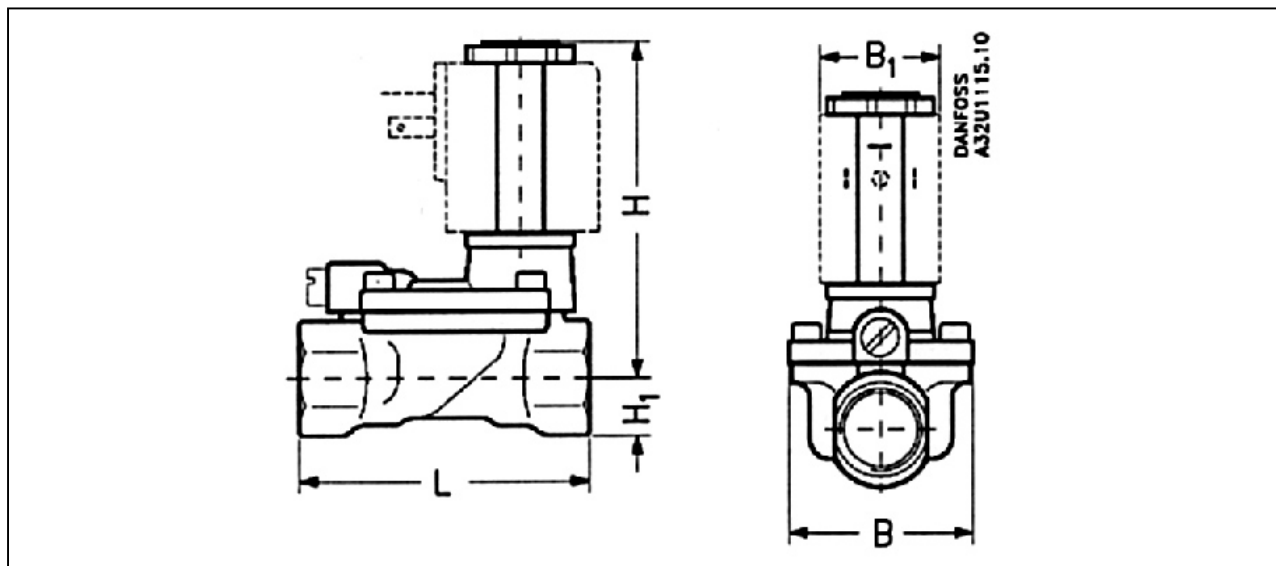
Габаритные и присоединительные размеры соленоидного клапана.
